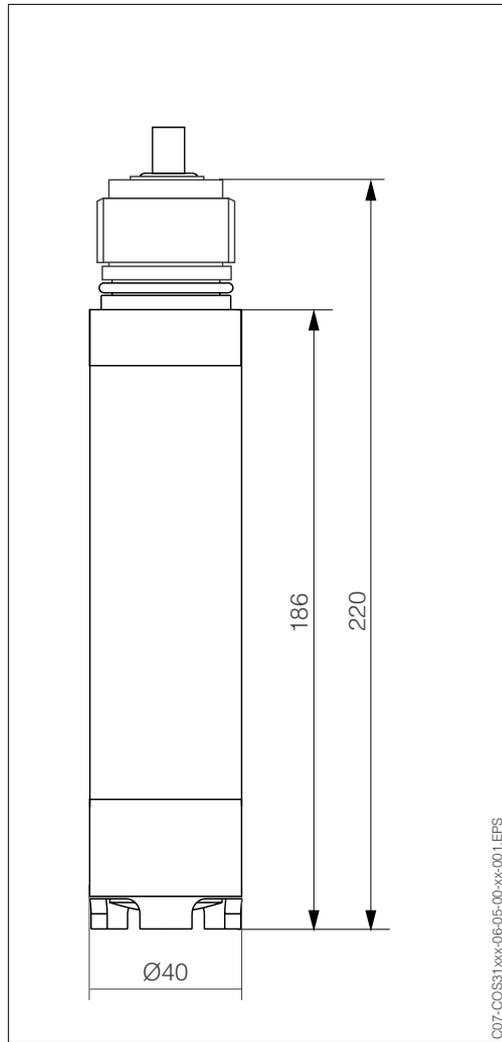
Dimensiones para la versión COS 31 con cable fijo
